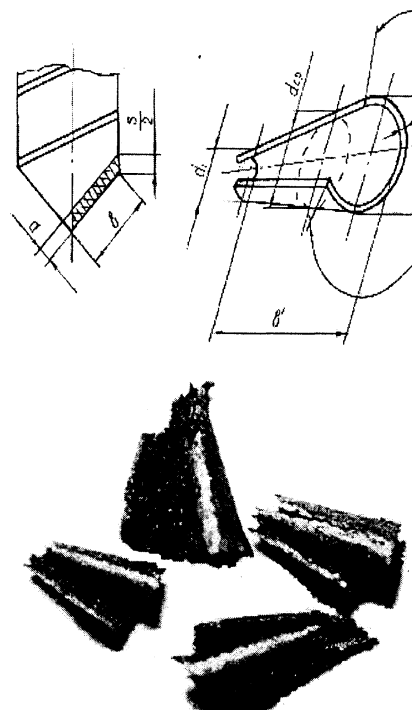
Модель и вид частиц дробленной стружки при сверлении стали 45 шнековым сверлом
